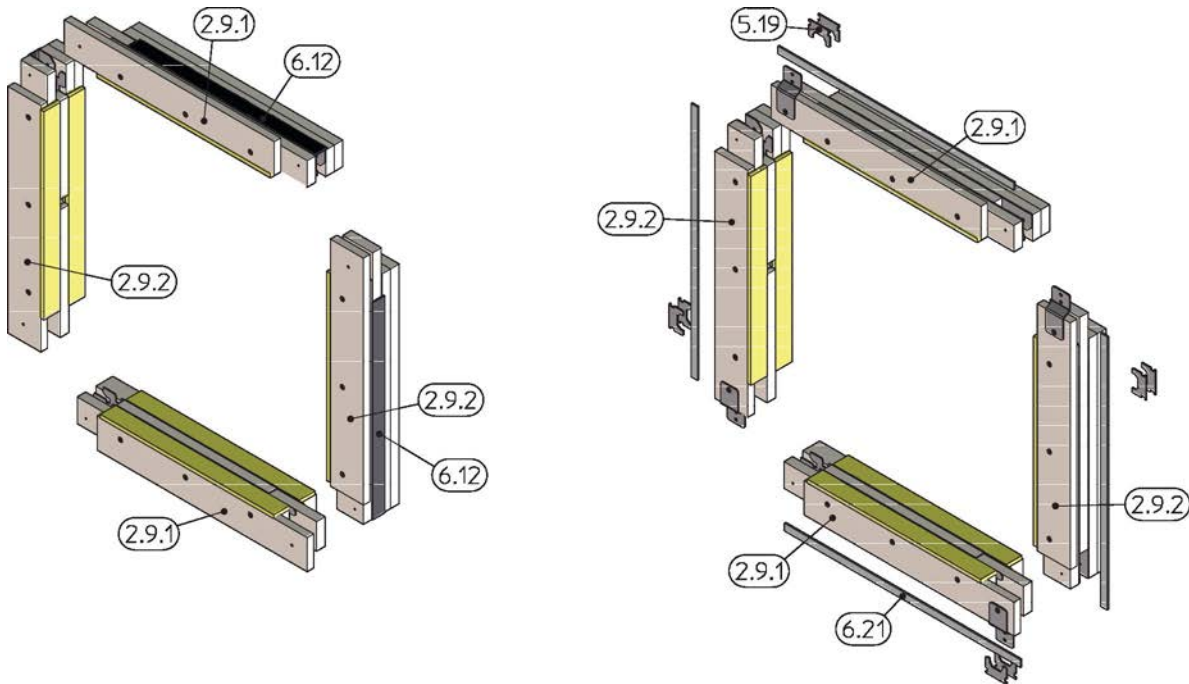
Montage Einbausatz ES für Trockeneinbau
